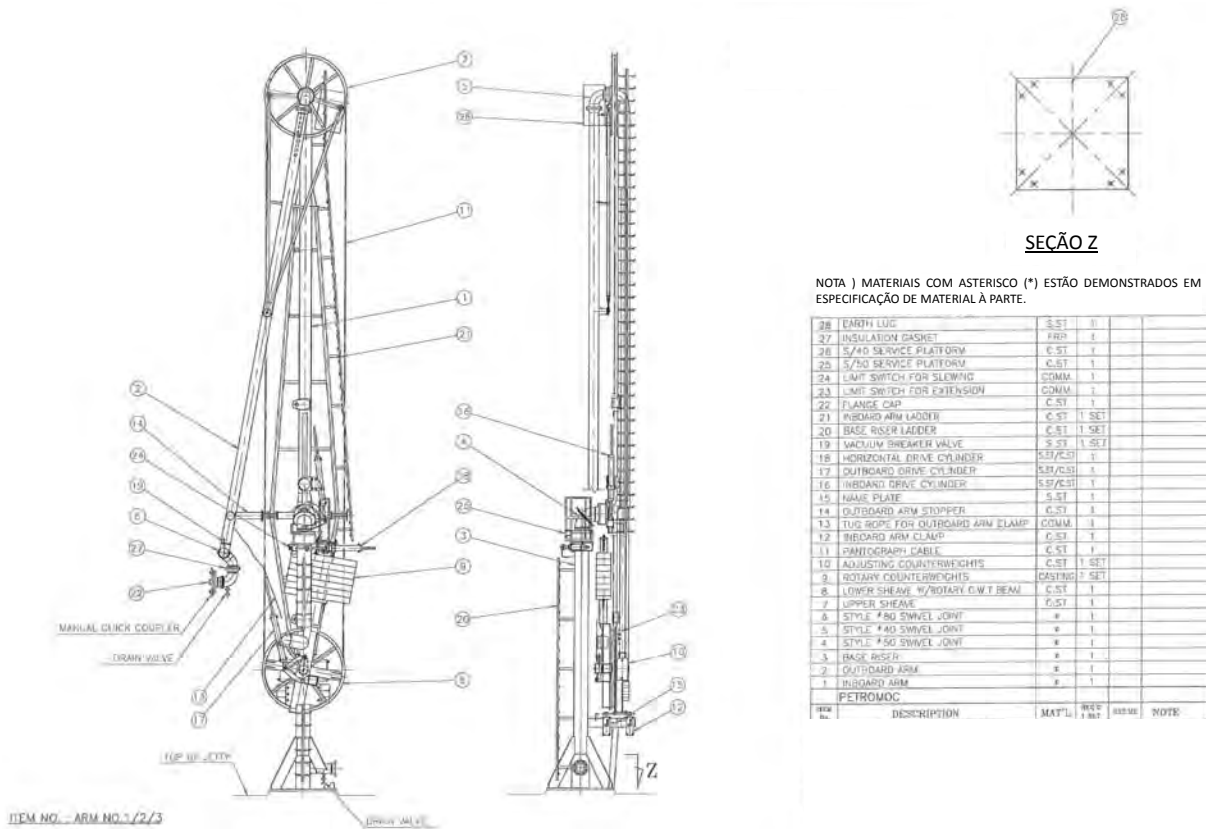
Plano Geral do Braço de Carregamento
